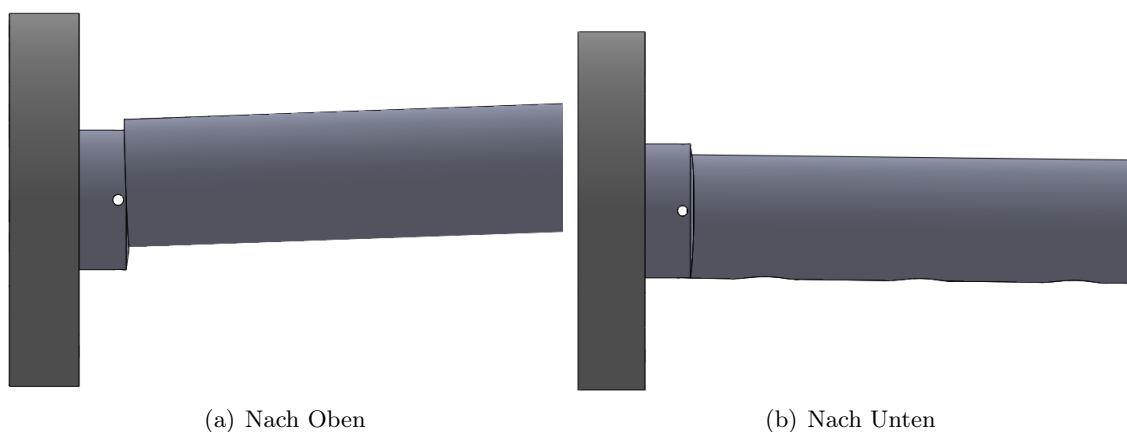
Die Bewegung des Stabes auf dem Sockel. Der Sockel wird am Manipulatorflansch befestigt, während das Rohr mittels starken Federn mit dem Sockel verbunden werden.
